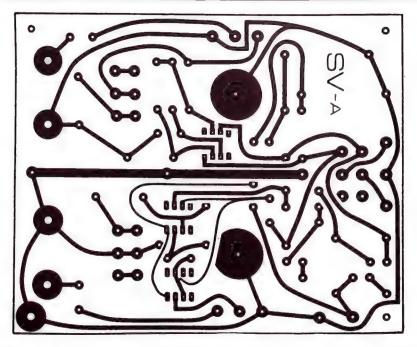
Der Print nimmt nicht nur die Elektronik, sondern auch die meisten mechanischen Bauteile auf.
